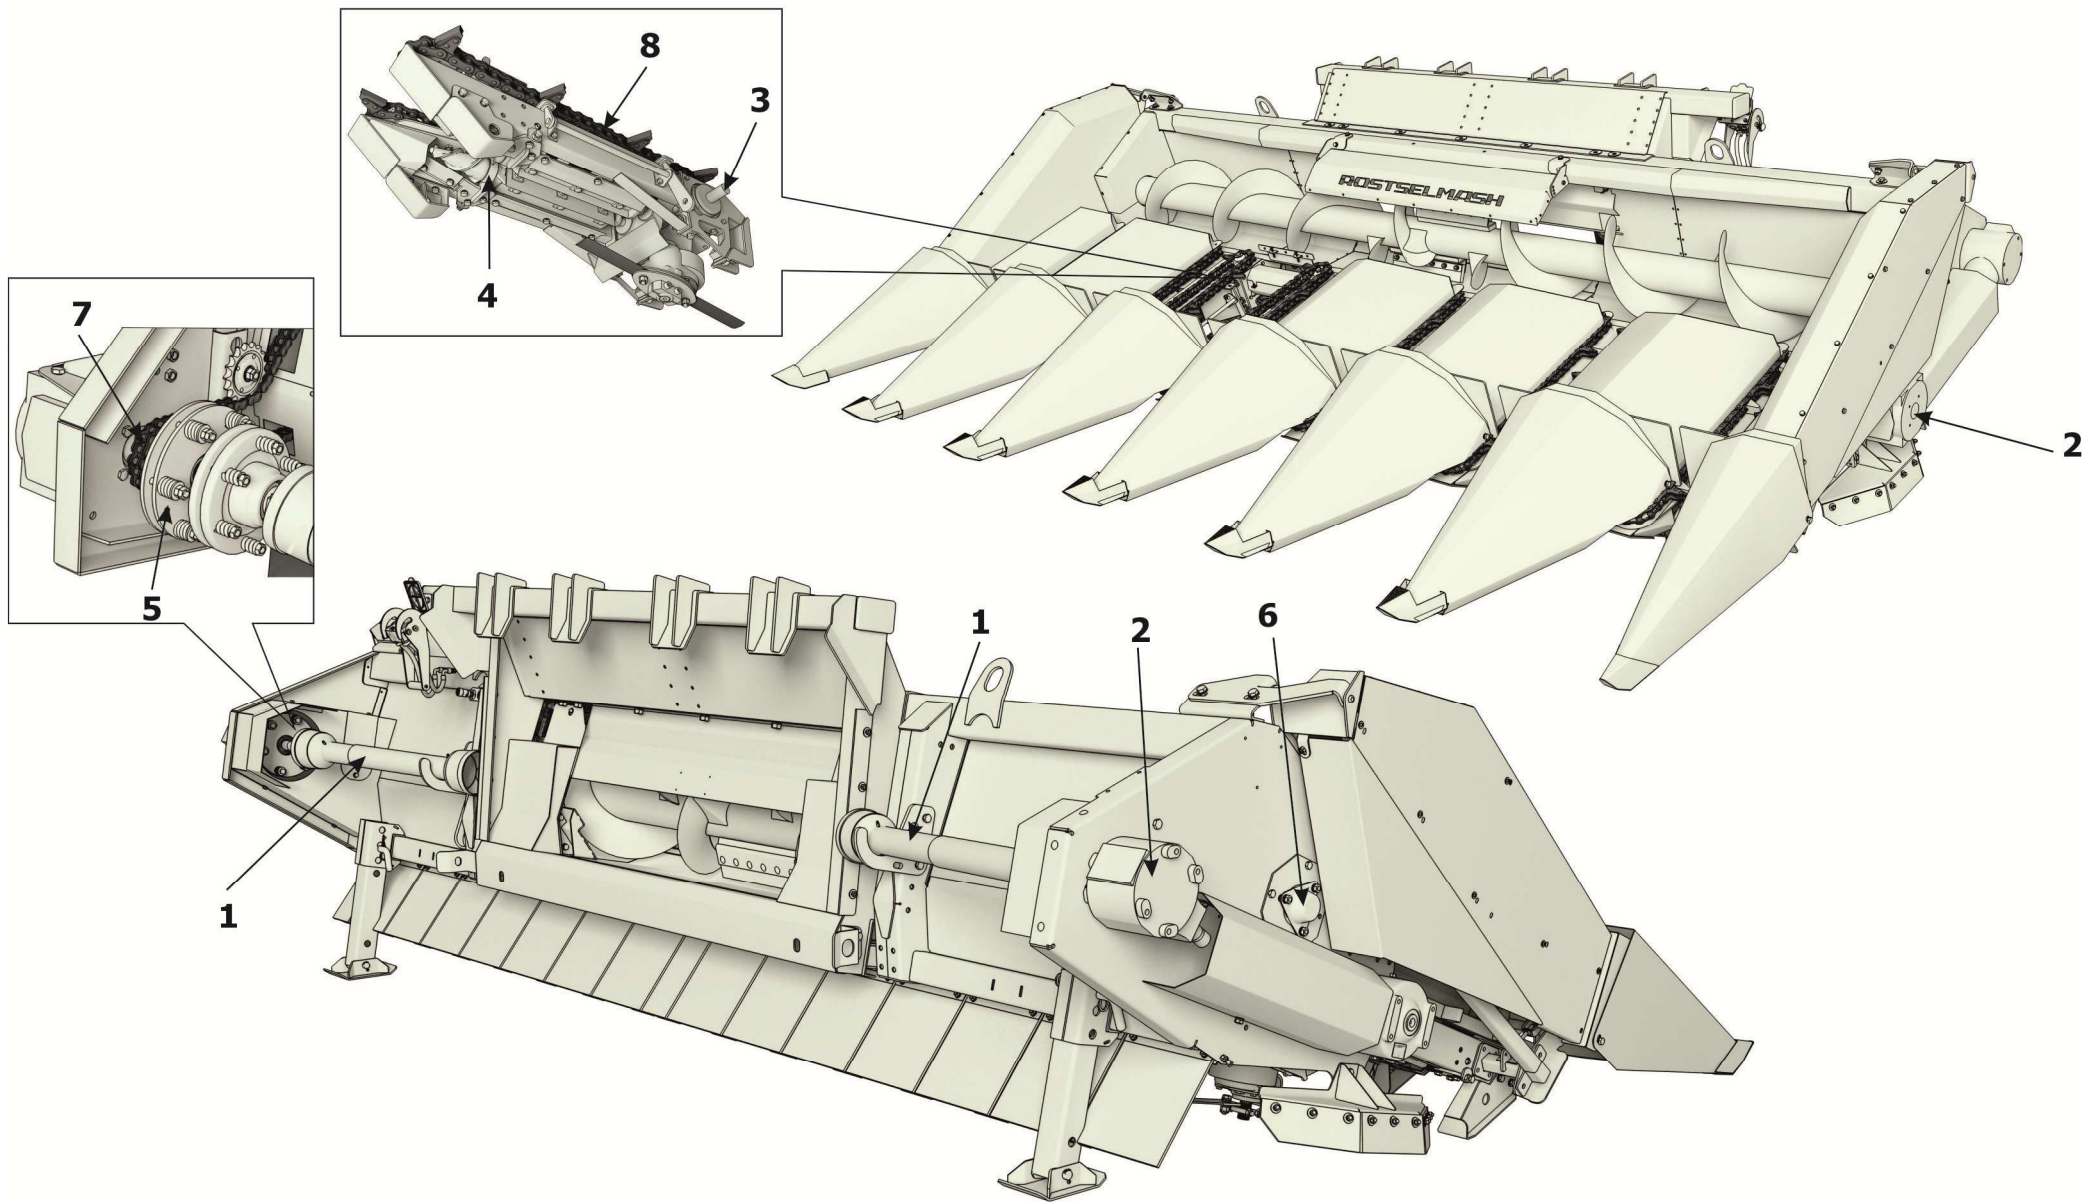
Схема смазки приспособления ППК-61-75
